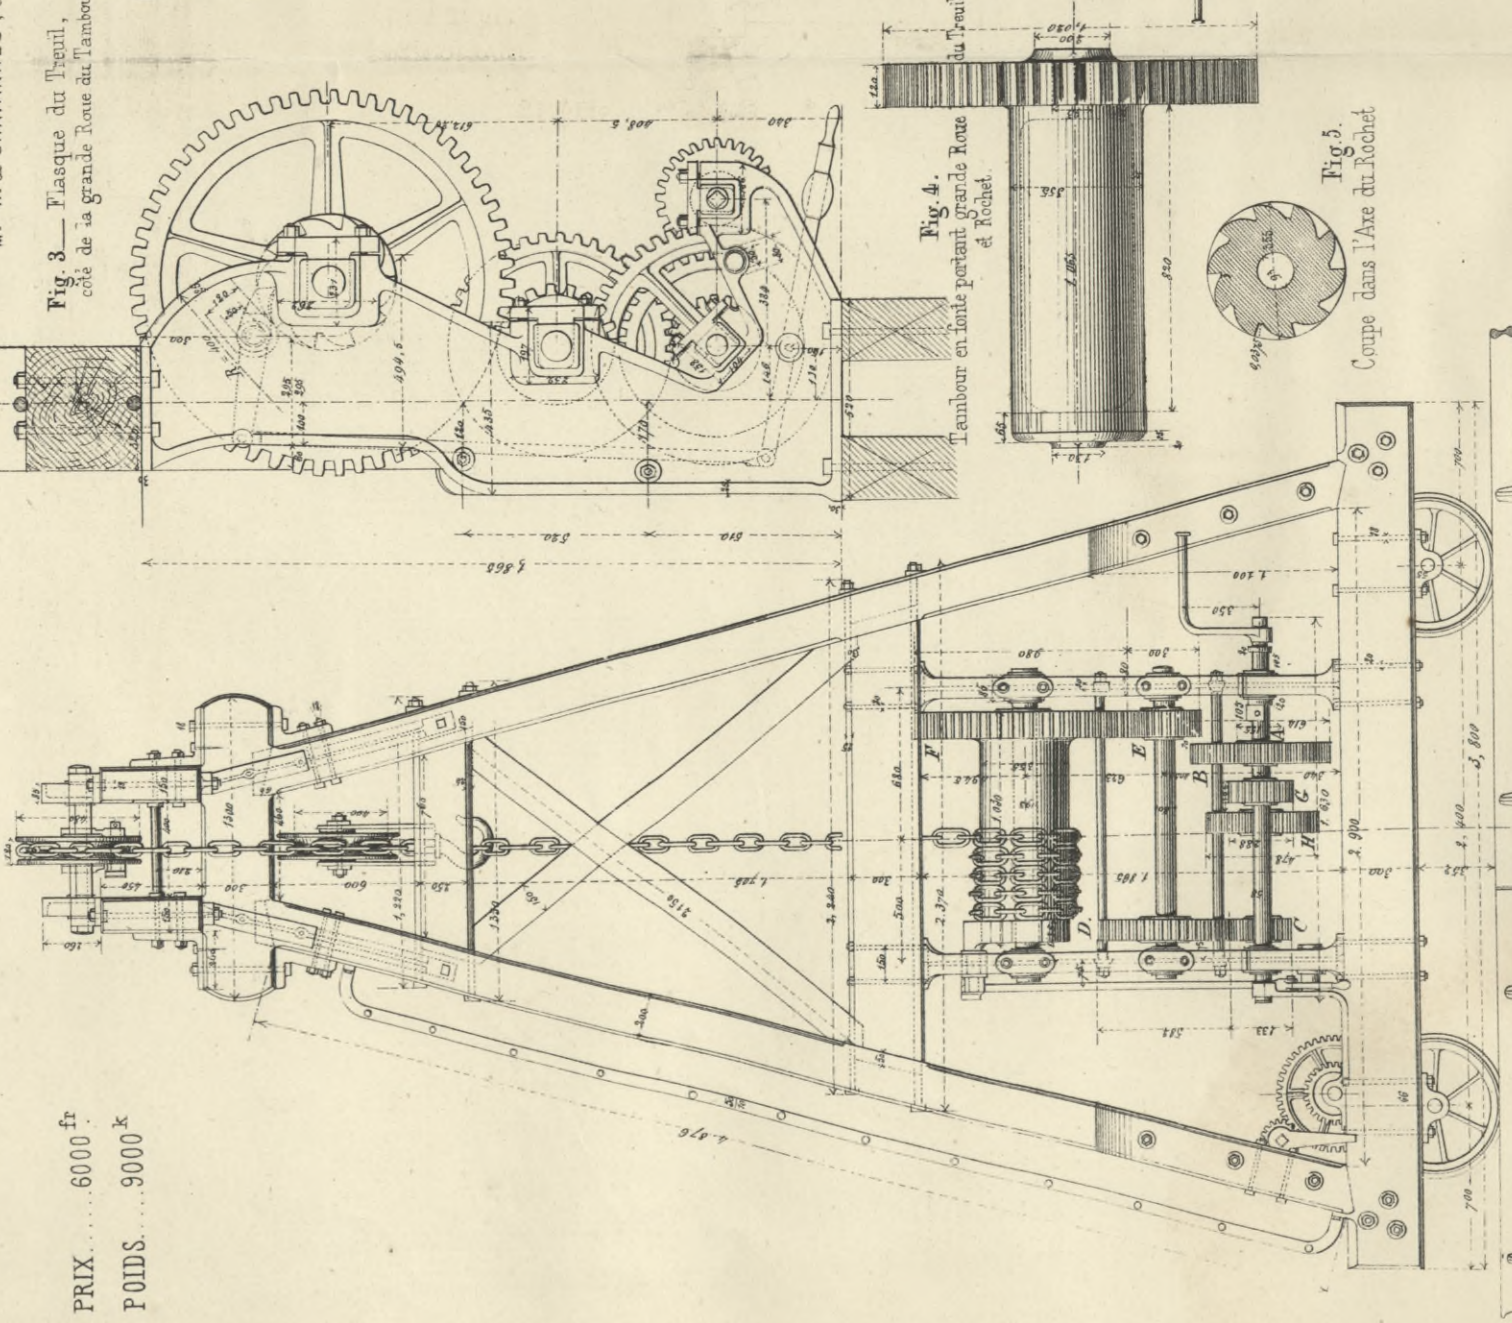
Flaque du Treuil, côté de la grande Roue du Tambour.
